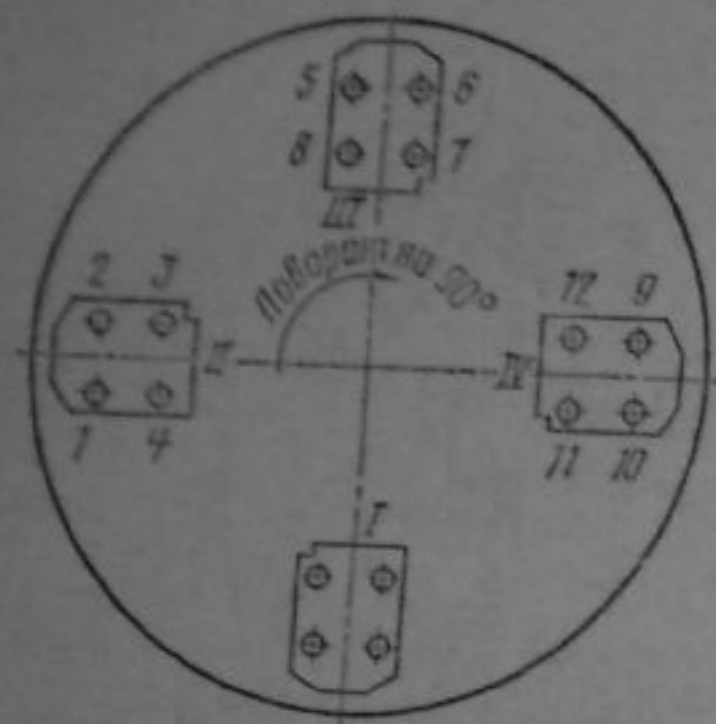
Схема расположения позиций 12-шпиндельного агрегатного вертикально-сверлильного станка для обработки корпуса (1—12 — номера шпинделей)
